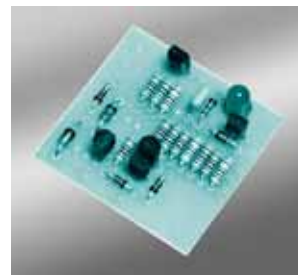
, 3 - Plošné spoje a příklad rozmístění součástek
